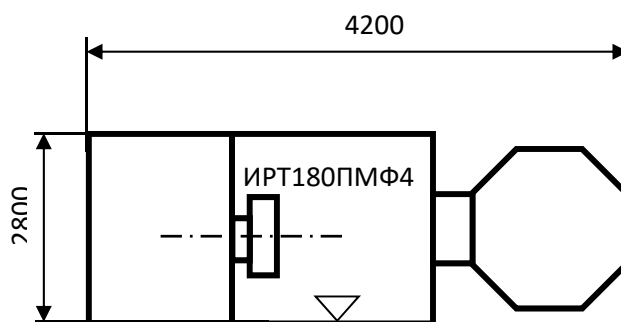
Токарный многоцелевой станок мод. ИРТ180ПМФ4
